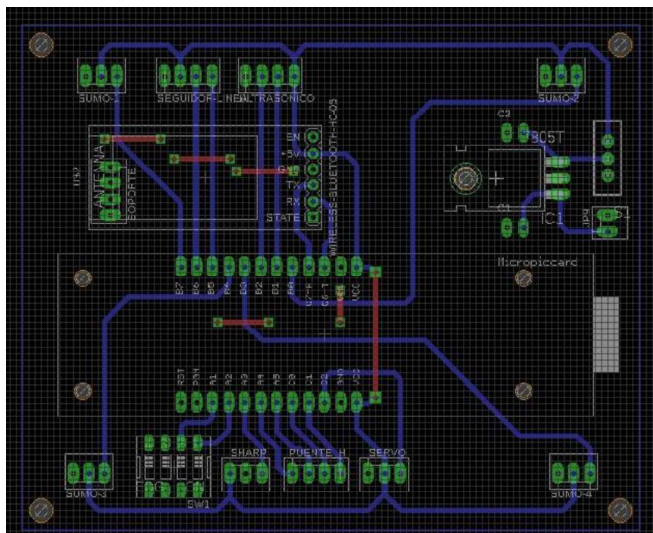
Diseño PCB de la tarjeta de control del mini robot.
